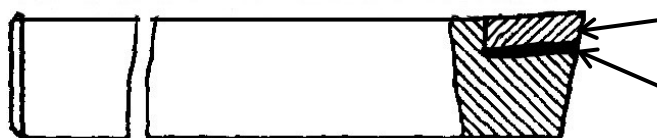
Схема конструкции резца с напаянной пластиной из быстрорежущей стали (1 – державка, 2 – режущая пластина, 3 – припой)
